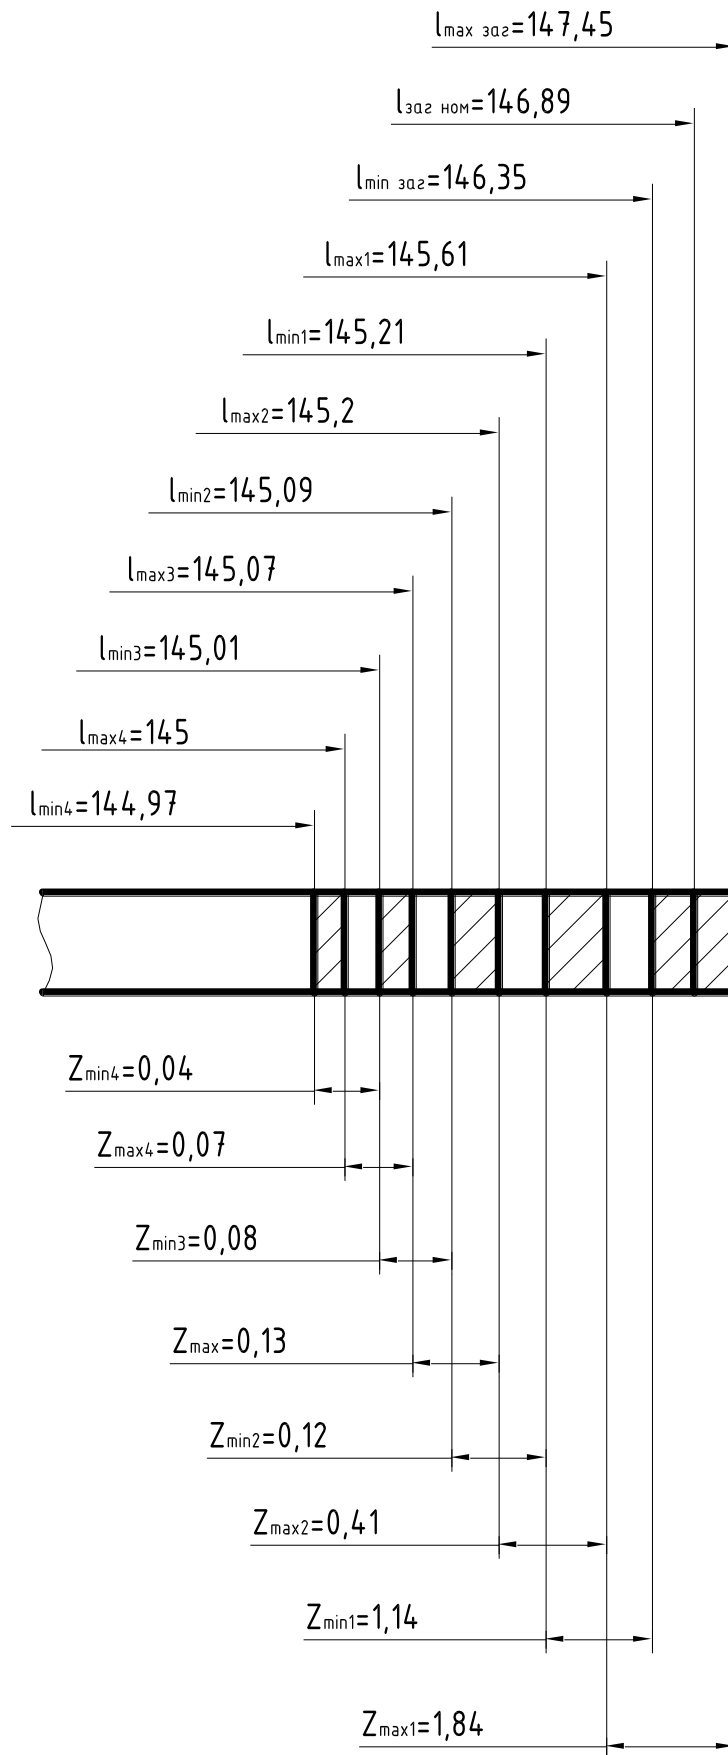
Схема графічного розташування припусків і допусків на оброблення площини 60x290 ($l = 145$ мм)
